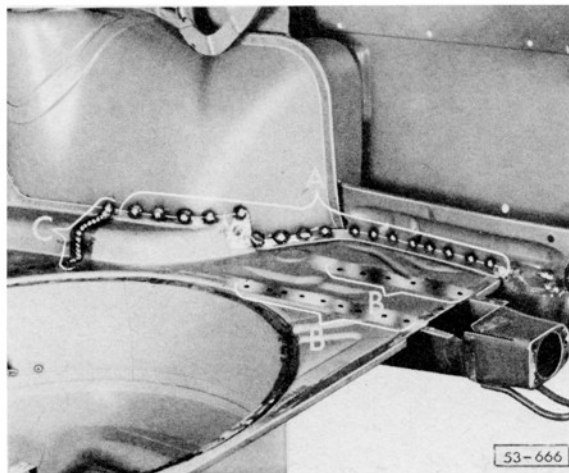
Kofferboden hinten – Teilstück einschweißen.
